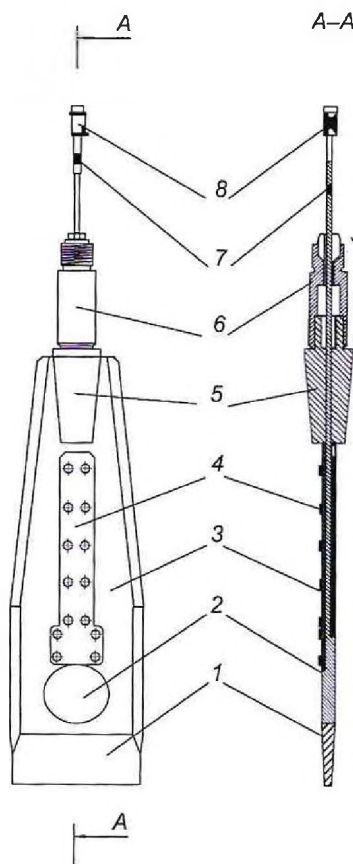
Конструкция зонда: 1 – наконечник; 2 – датчик давления грунта; 3 – рабочая часть зонда; 4 – крышка канала вывода кабеля; 5 – конус; 6 – переходник с резьбой под штангу; 7 – кабель; 8 – разъем
